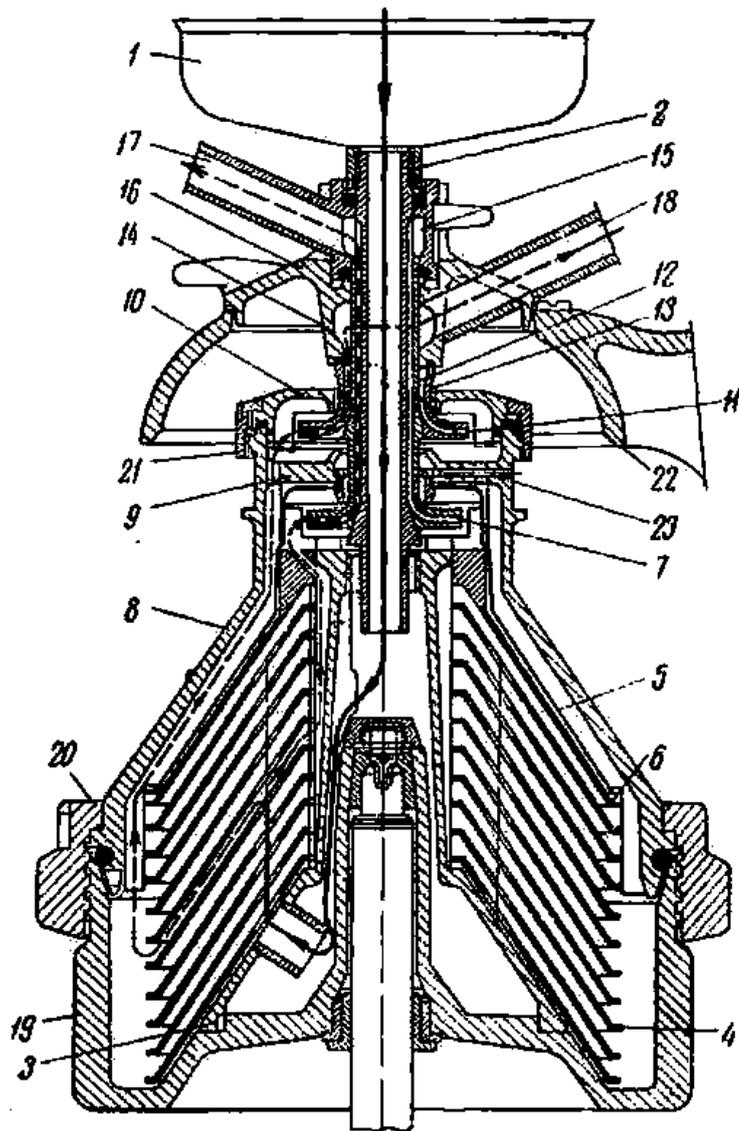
Барабан полугерметического сепаратора: 1 - поплавковая камера; 2 - центральная трубка; 3 - тарелкодержатель; 4 - пакет тарелок; 5 - разделительная тарелка; 6 - верхняя тарелка; 7 - напорный диск для сливок; 8 - крышка барабана; 9 - перегородка; 10 - верхняя крышка; 11 - напорный диск для обезжиренного молока; 12 - трубка напорного диска для сливок; 13 - трубка напорного диска для обезжиренного молока; 14 - кольцевая камера для обезжиренного молока; 15 - кольцевая камера для сливок; 16 - приемник; 17 - патрубок для отвода сливок; 18 - патрубок для отвода обезжиренного молока; 19 - корпус барабана; 20 и 21 - затяжные гайки барабана и крышки; 22 - заградительный колпак; 23 - горизонтальный канал в перегородке
